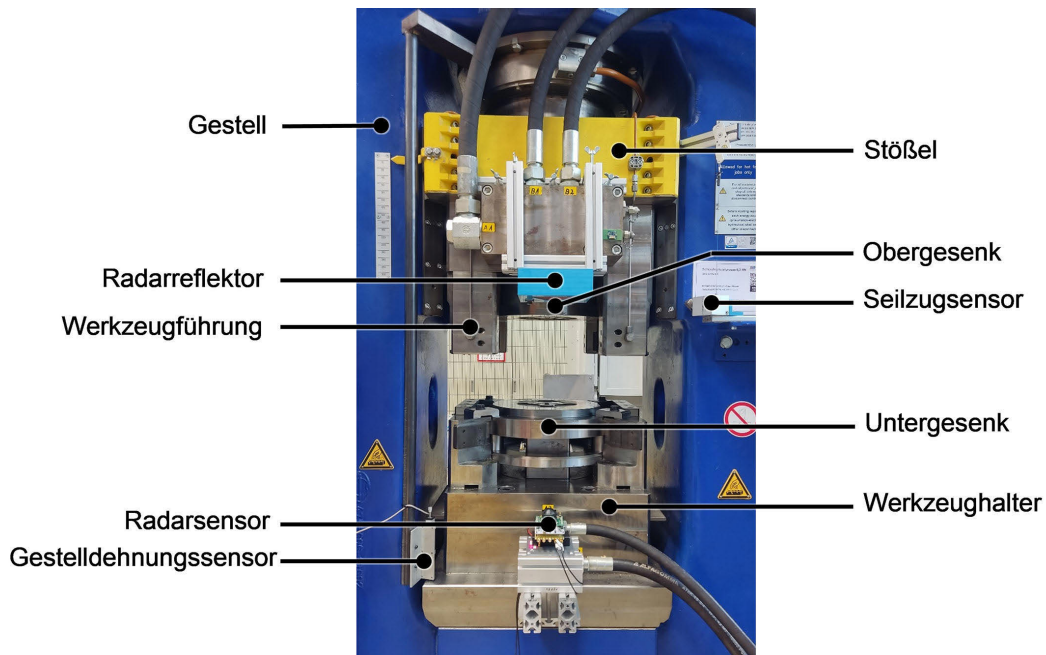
Eingesetzte Umformpresse mit Werkzeugen und Sensorik. Foto: FHF BTU
